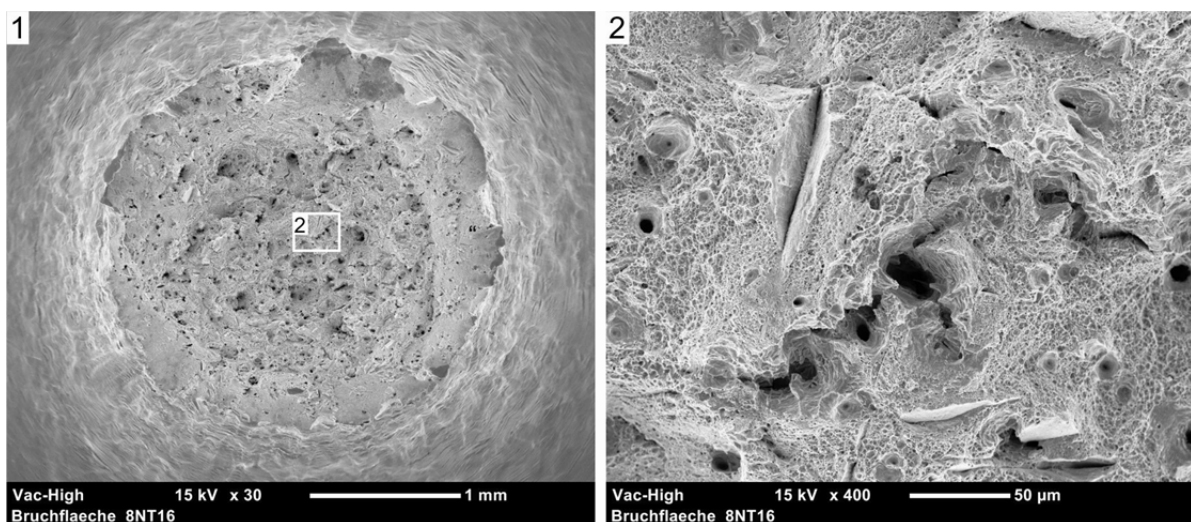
Bruchfläche einer Kerbzugprobe aus der austenitischen WEZ (REM-Aufnahme)
